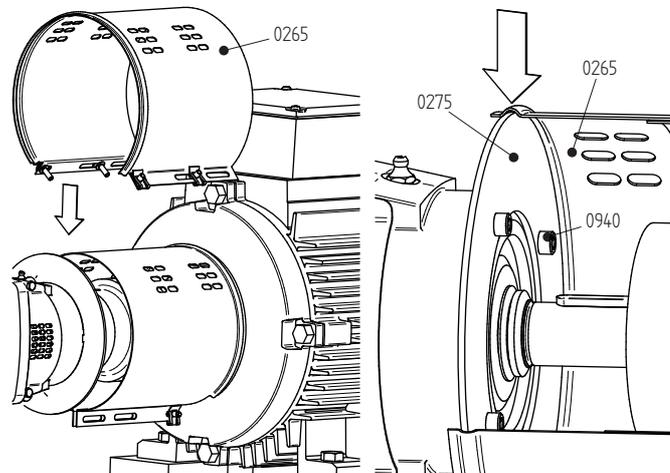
Montieren der Haube auf der Pumpenseite.
